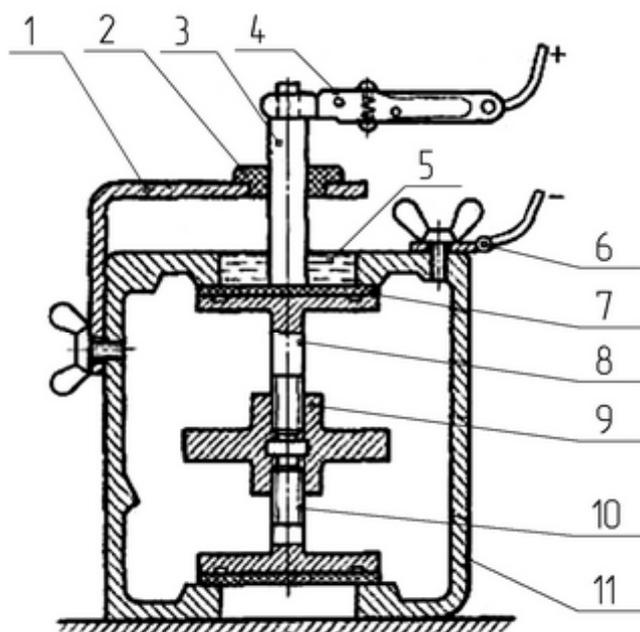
Приспособление для железнения вне ванны: 1 – угольник для центрирования и крепления анода; 2 – эбонитовая втулка; 3 – анод; 4 – быстросъемный зажим; 5 – электролит; 6 – катодный контакт; 7 – резиновая пластина; 8 – верхний прижим с левой резьбой; 9 – зажимная гайка; 10 – нижний прижим с правой резьбой; 11 – картер коробки передач
